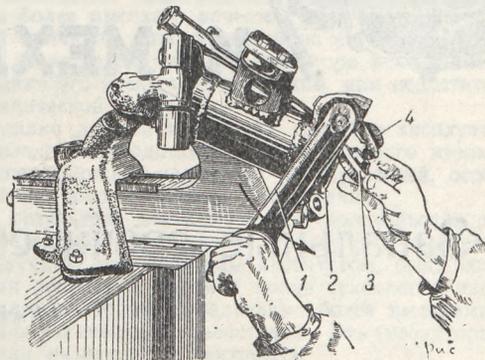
Установка пружины и чашки в цилиндр подвески.
